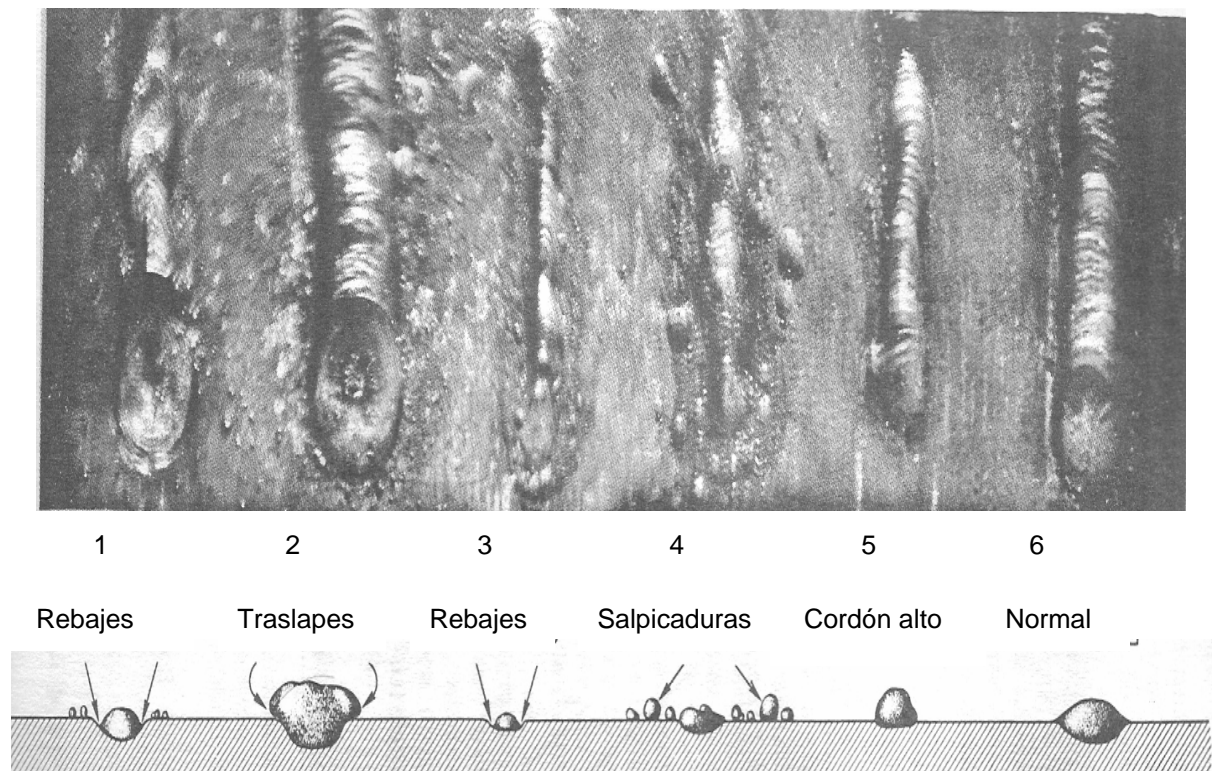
Diferente fallas en cordones de soldadura
